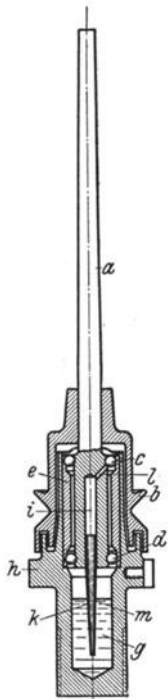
Spindel mit Kugellagerung (Schweinfurter-Präzisions-Kugellager-Werke).
